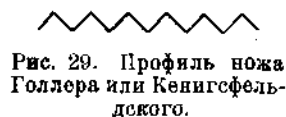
Профиль ножа Голлера или Кенигфельдского.
